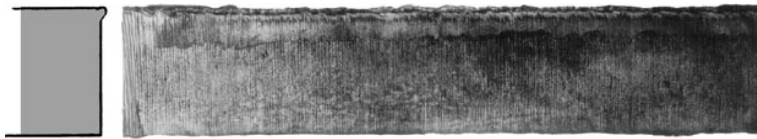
Boquilla de oxicortes demasiado lejos.
